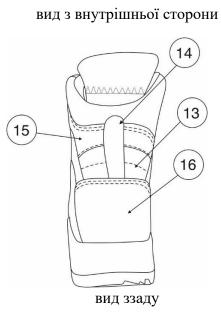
Конструкція та орієнтовний зовнішній вигляд предмета
